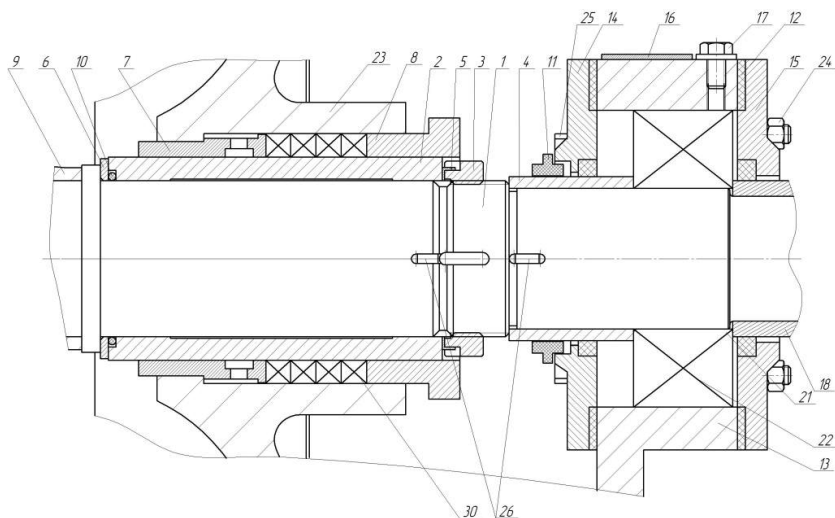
Доработка сальникового уплотнения с быстросъемной рубашкой (насос ЦНС 300): 1 – вал; 2 – рубашка вала; 3 – гайка круглая специальная; 4 – тулка; 5 – шайба предохранительная для установочных гаек; 6 – кольцо; 7 – втулка гидрозатвора; 8 – втулка сальника; 9 – колесо рабочее первой ступени; 10 – кольцо резиновое; 11 – ольцо отбойное; 12 – прокладка; 13 – кронштейн передний; 14 – крышка подшипника; 15 – крышка передняя; 16 – табличка; 17 – робка; 18 – втулка; 21 – манжета 12-105x130-1 ГОСТ 8752-79; 22 – подшипник 3618 ГОСТ5721-75; 23 – крышка всасывания; 24 – гайка М12.4 ГОСТ5915-70; 25 – болт М12х140.36 ГОСТ7795-70; 26 – шпонка 6х6х14 ГОСТ 23360-78; 30 – набивка сквозного плетения марки АП-3116х16 ГОСТ5152-84
